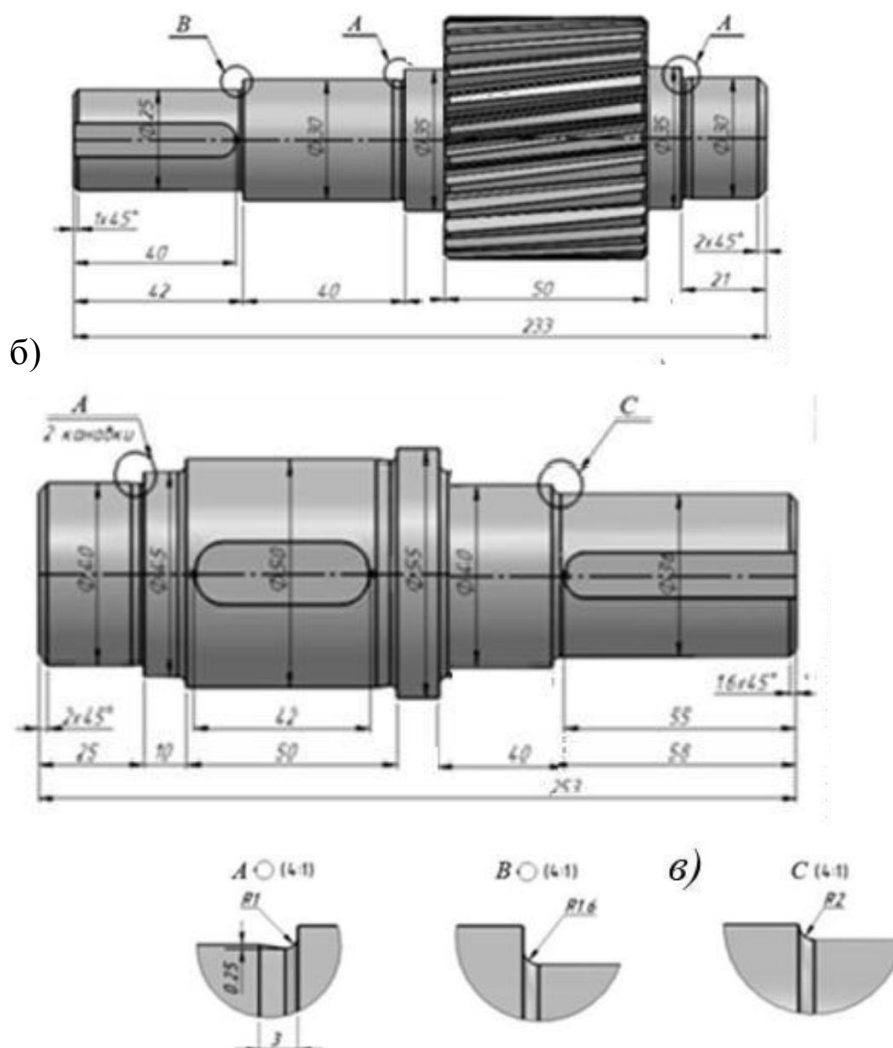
Примеры конструктивного исполнения валов: *а* – ведущий вал в сборе с подшипниками; *б* – ведущий вал; *в* – ведомый вал
